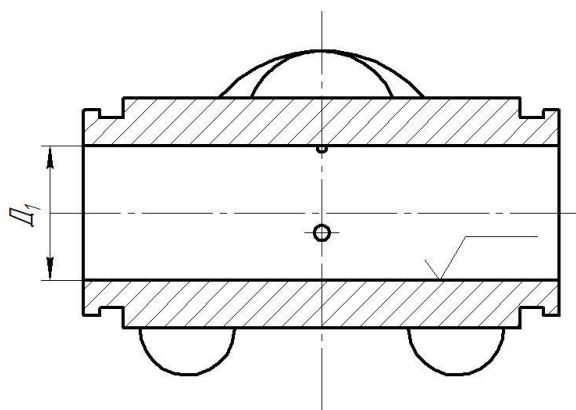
Тормозной цилиндр колёсный (главный/задний/передний)
